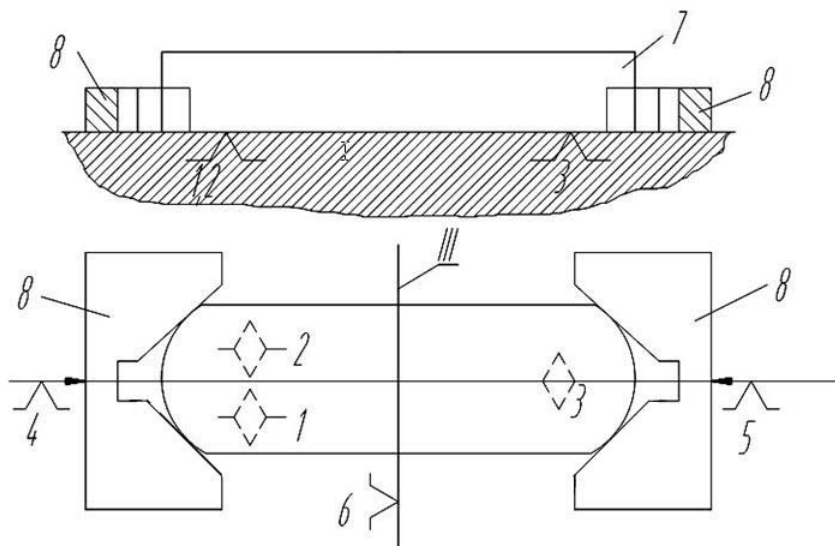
Технологические базы: I – установочная явная база заготовки; II – направляющая скрытая база заготовки; 1...6 – опорные точки; 7 – заготовка; 8 – губки самоцентрирующих тисков
